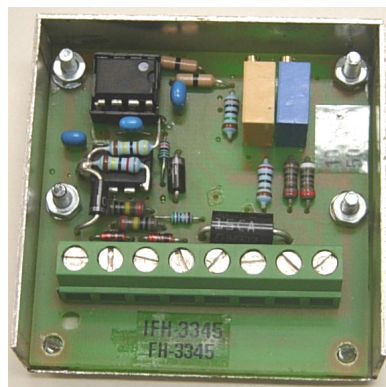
Placa do circuito integrador (tampa metálica removida)
